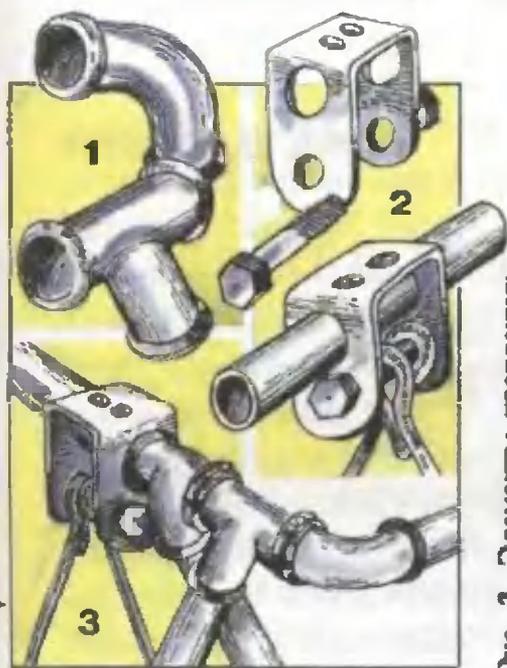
Элементы крепления: 1 — водопроводное коллено и водопроводный тройник; 2 — конструкция самодельной скобы, скрепляющей кольца строп качелей; 3 — узел углового соединения со стойками.
